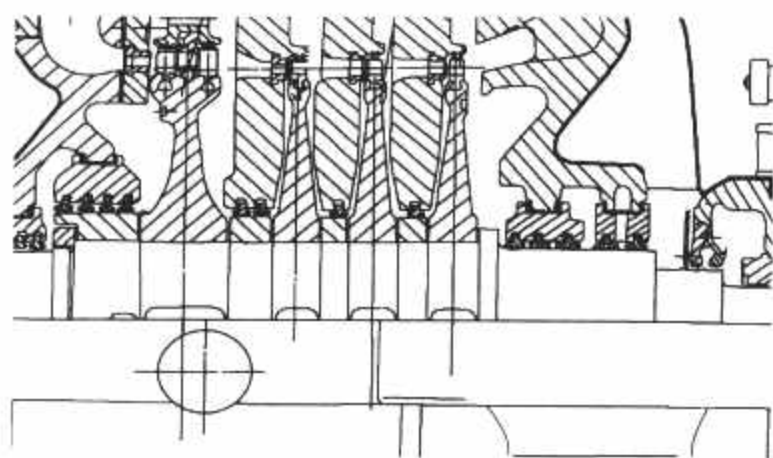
中压 6MW 背压式汽轮机剖面图
